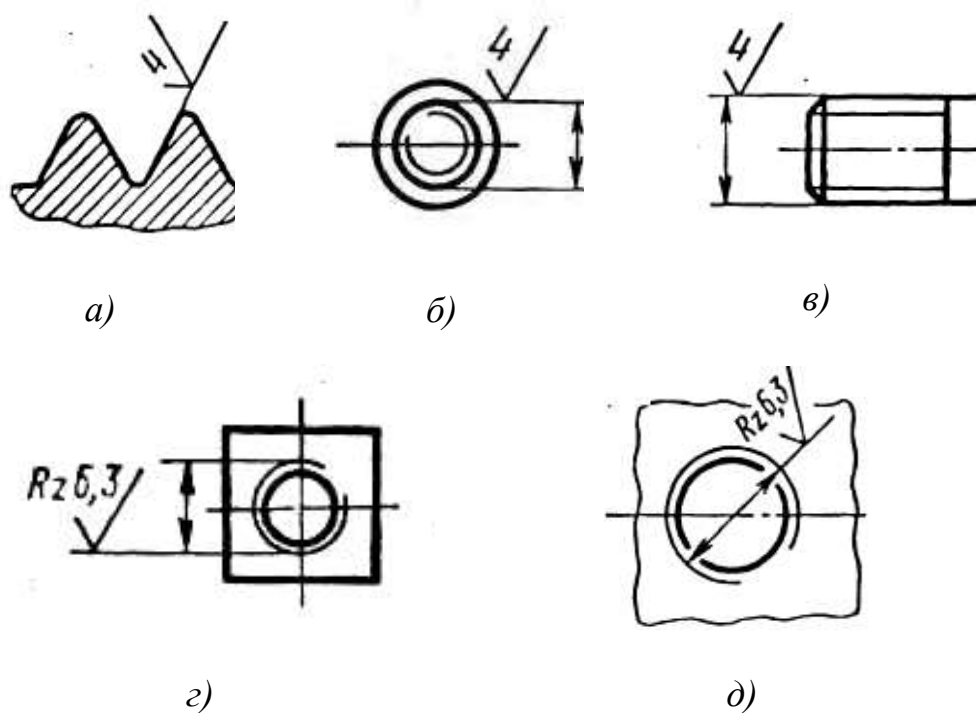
Обозначение шероховатости рабочих сторон резьбы.
